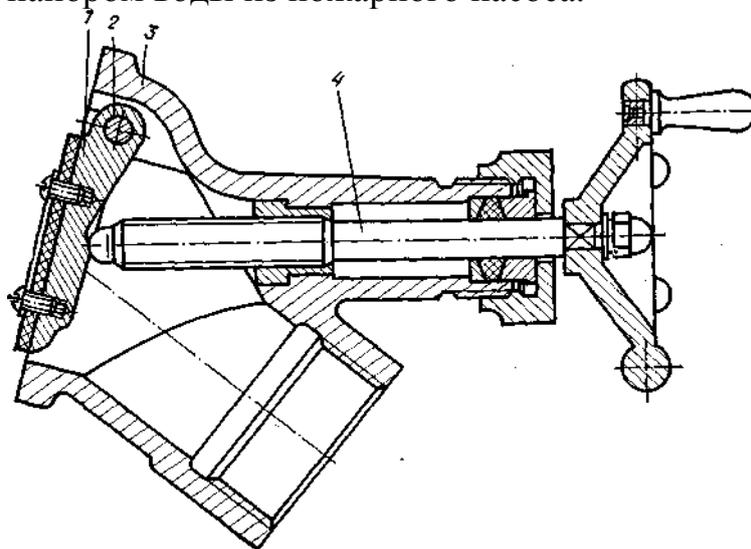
Напорная задвижка коллектора насоса ПН-40УА: 1 – клапан; 2 – ось; 3 – корпус; 4 – шпindelъ
